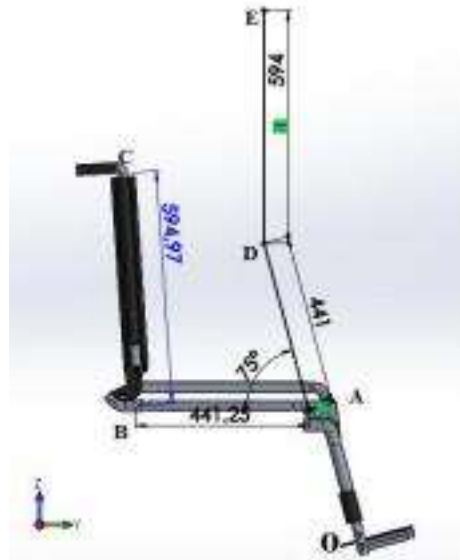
Cinemática mecanismo bipedestador - Silla de ruedas bipedestadora Fuente: Elaboración propia
